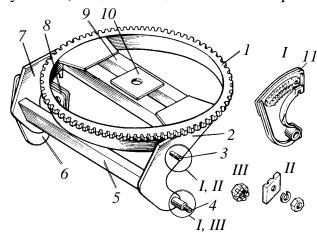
Поворотный круг: 1 – венец; 2, 7 – щеки; 3, 4 – пальцы; 5, 9 – балки; 6, 11 – кронштейн; 8 – проушина; 10 – плита; I, II, III – элементы крепления грейдерного отвала
